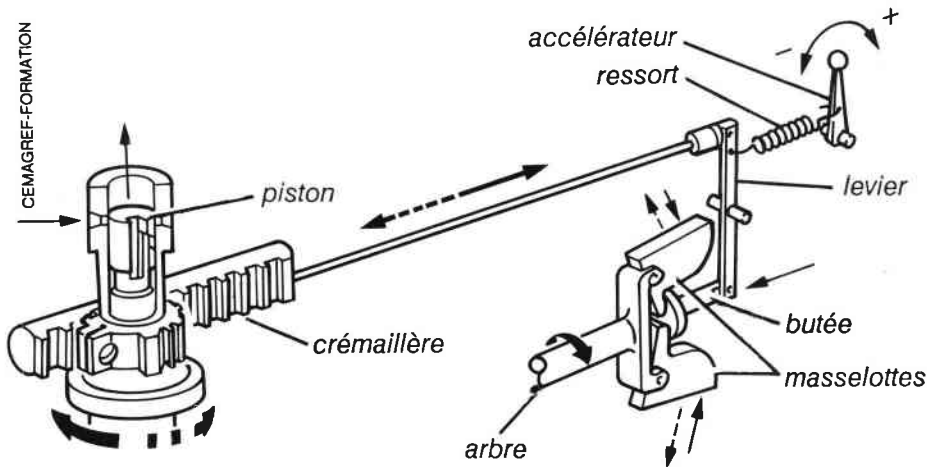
Principe d'action du régulateur centrifuge d'une pompe en ligne.
